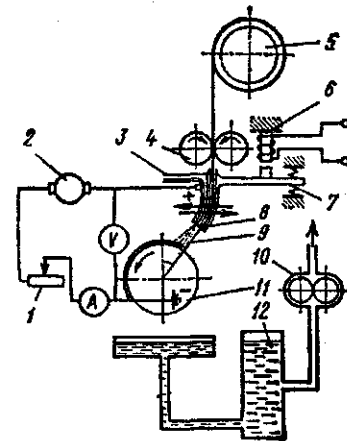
Схема установки для автоматической вибродуговой наплавки:
